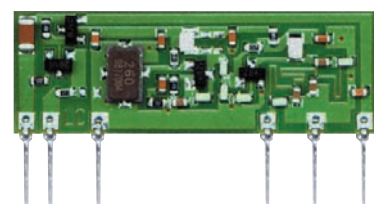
Le module Aurel TX8LAVSA05 vu côté soudures.
